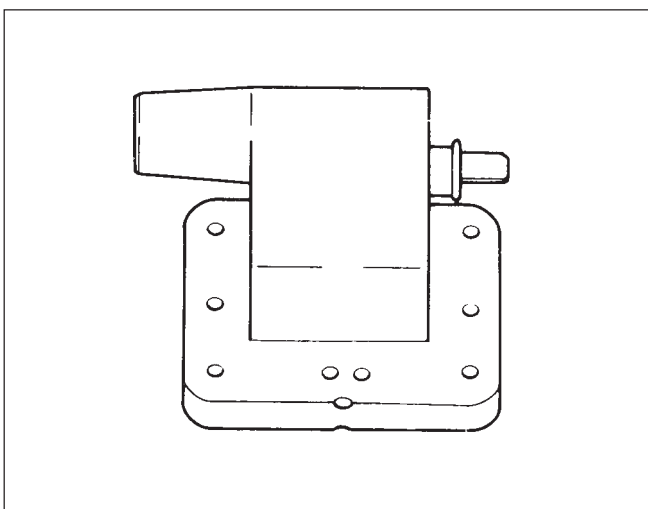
F – 3 Bobină de aprindere cu miez magnetic tip închis
